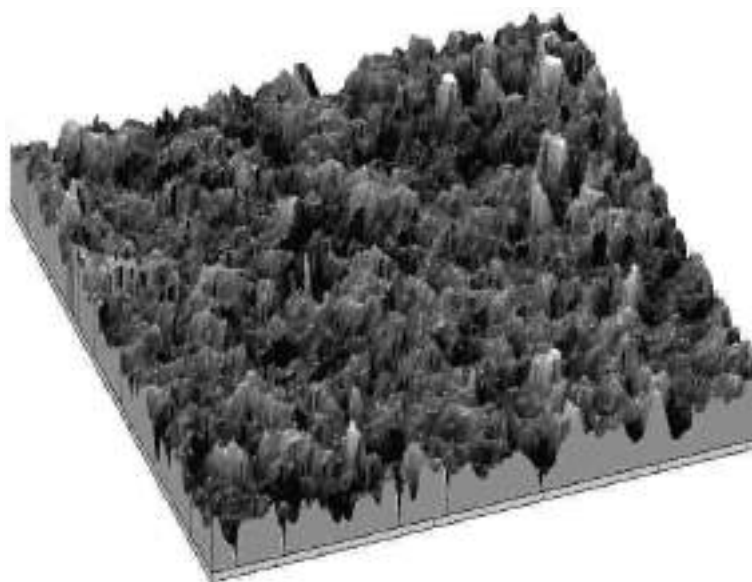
Змодельована поверхня після струйно-абразивної обробки
